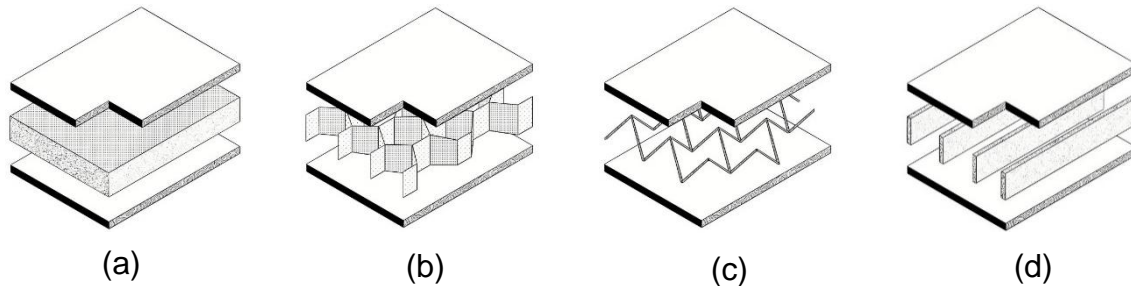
Tipos de estructuras más comunes en núcleos de paneles tipo sándwich: (a) espuma o sólido continuo, (b) estructura tipo panel, (c) estructura de barras y (d) *web-core*.
